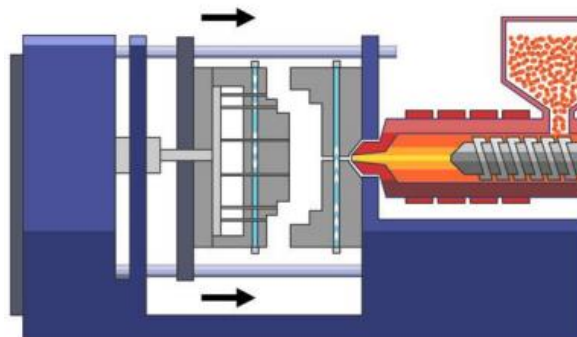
Fase I/Cierre del molde. Fuente: [G. Goitia Bollar](#).
